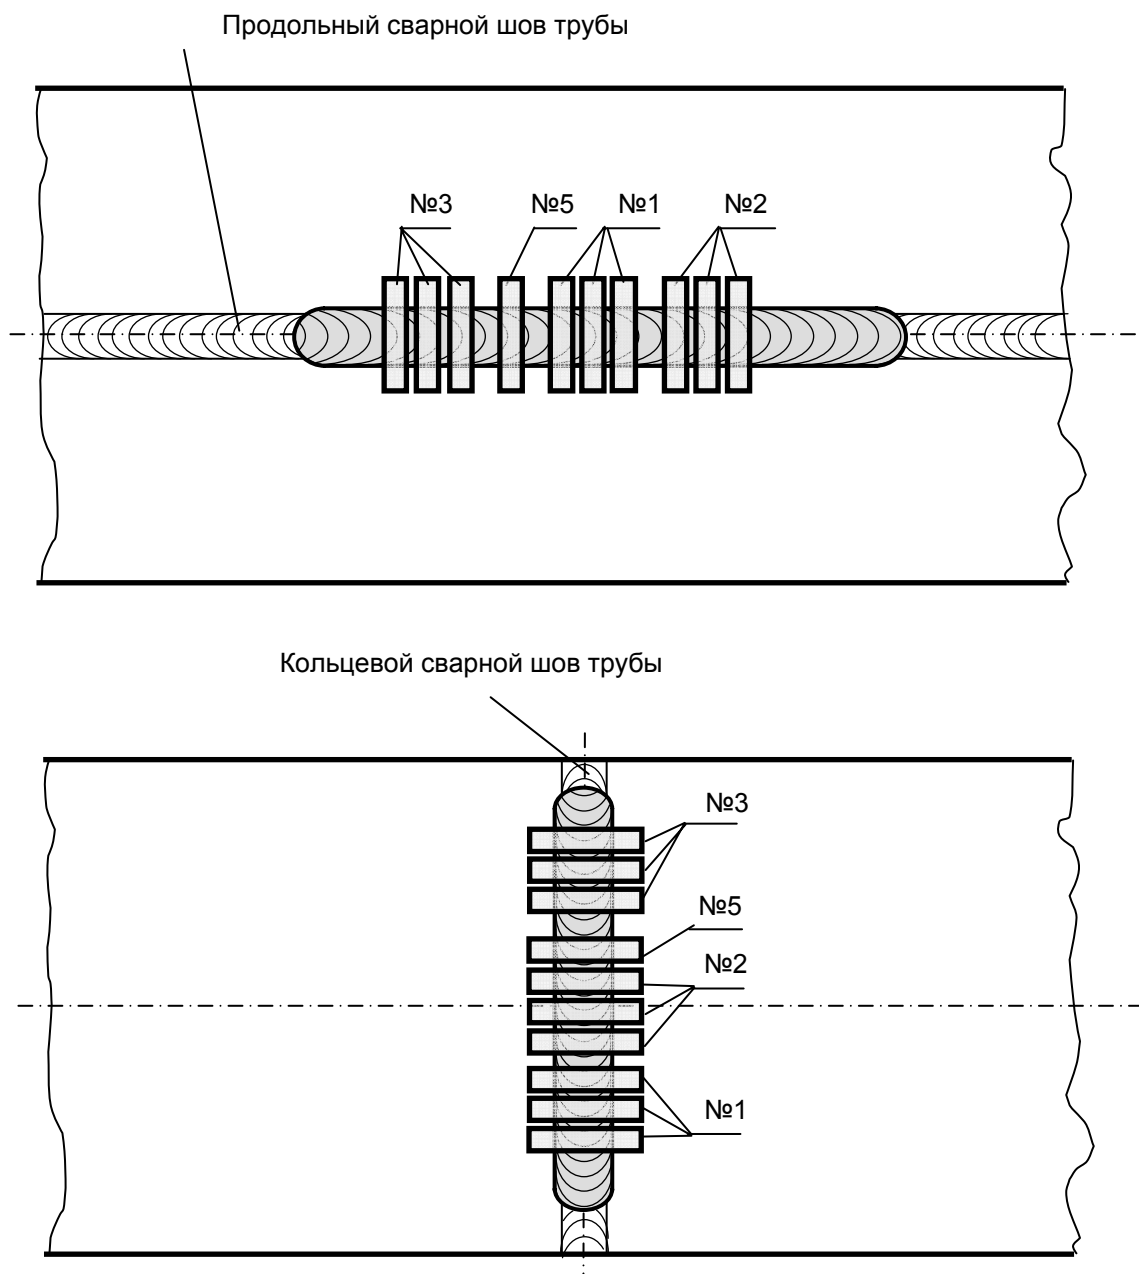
Схема вырезки образцов для механических испытаний при аттестации технологии ремонта сваркой (заваркой) в кольцевых и продольных сварных соединениях:
